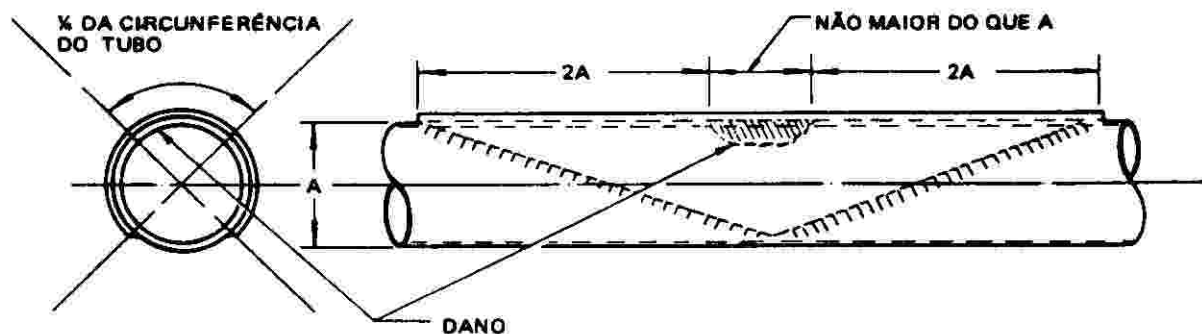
Reparo de Tubos por "Bacalhau" Soldado
